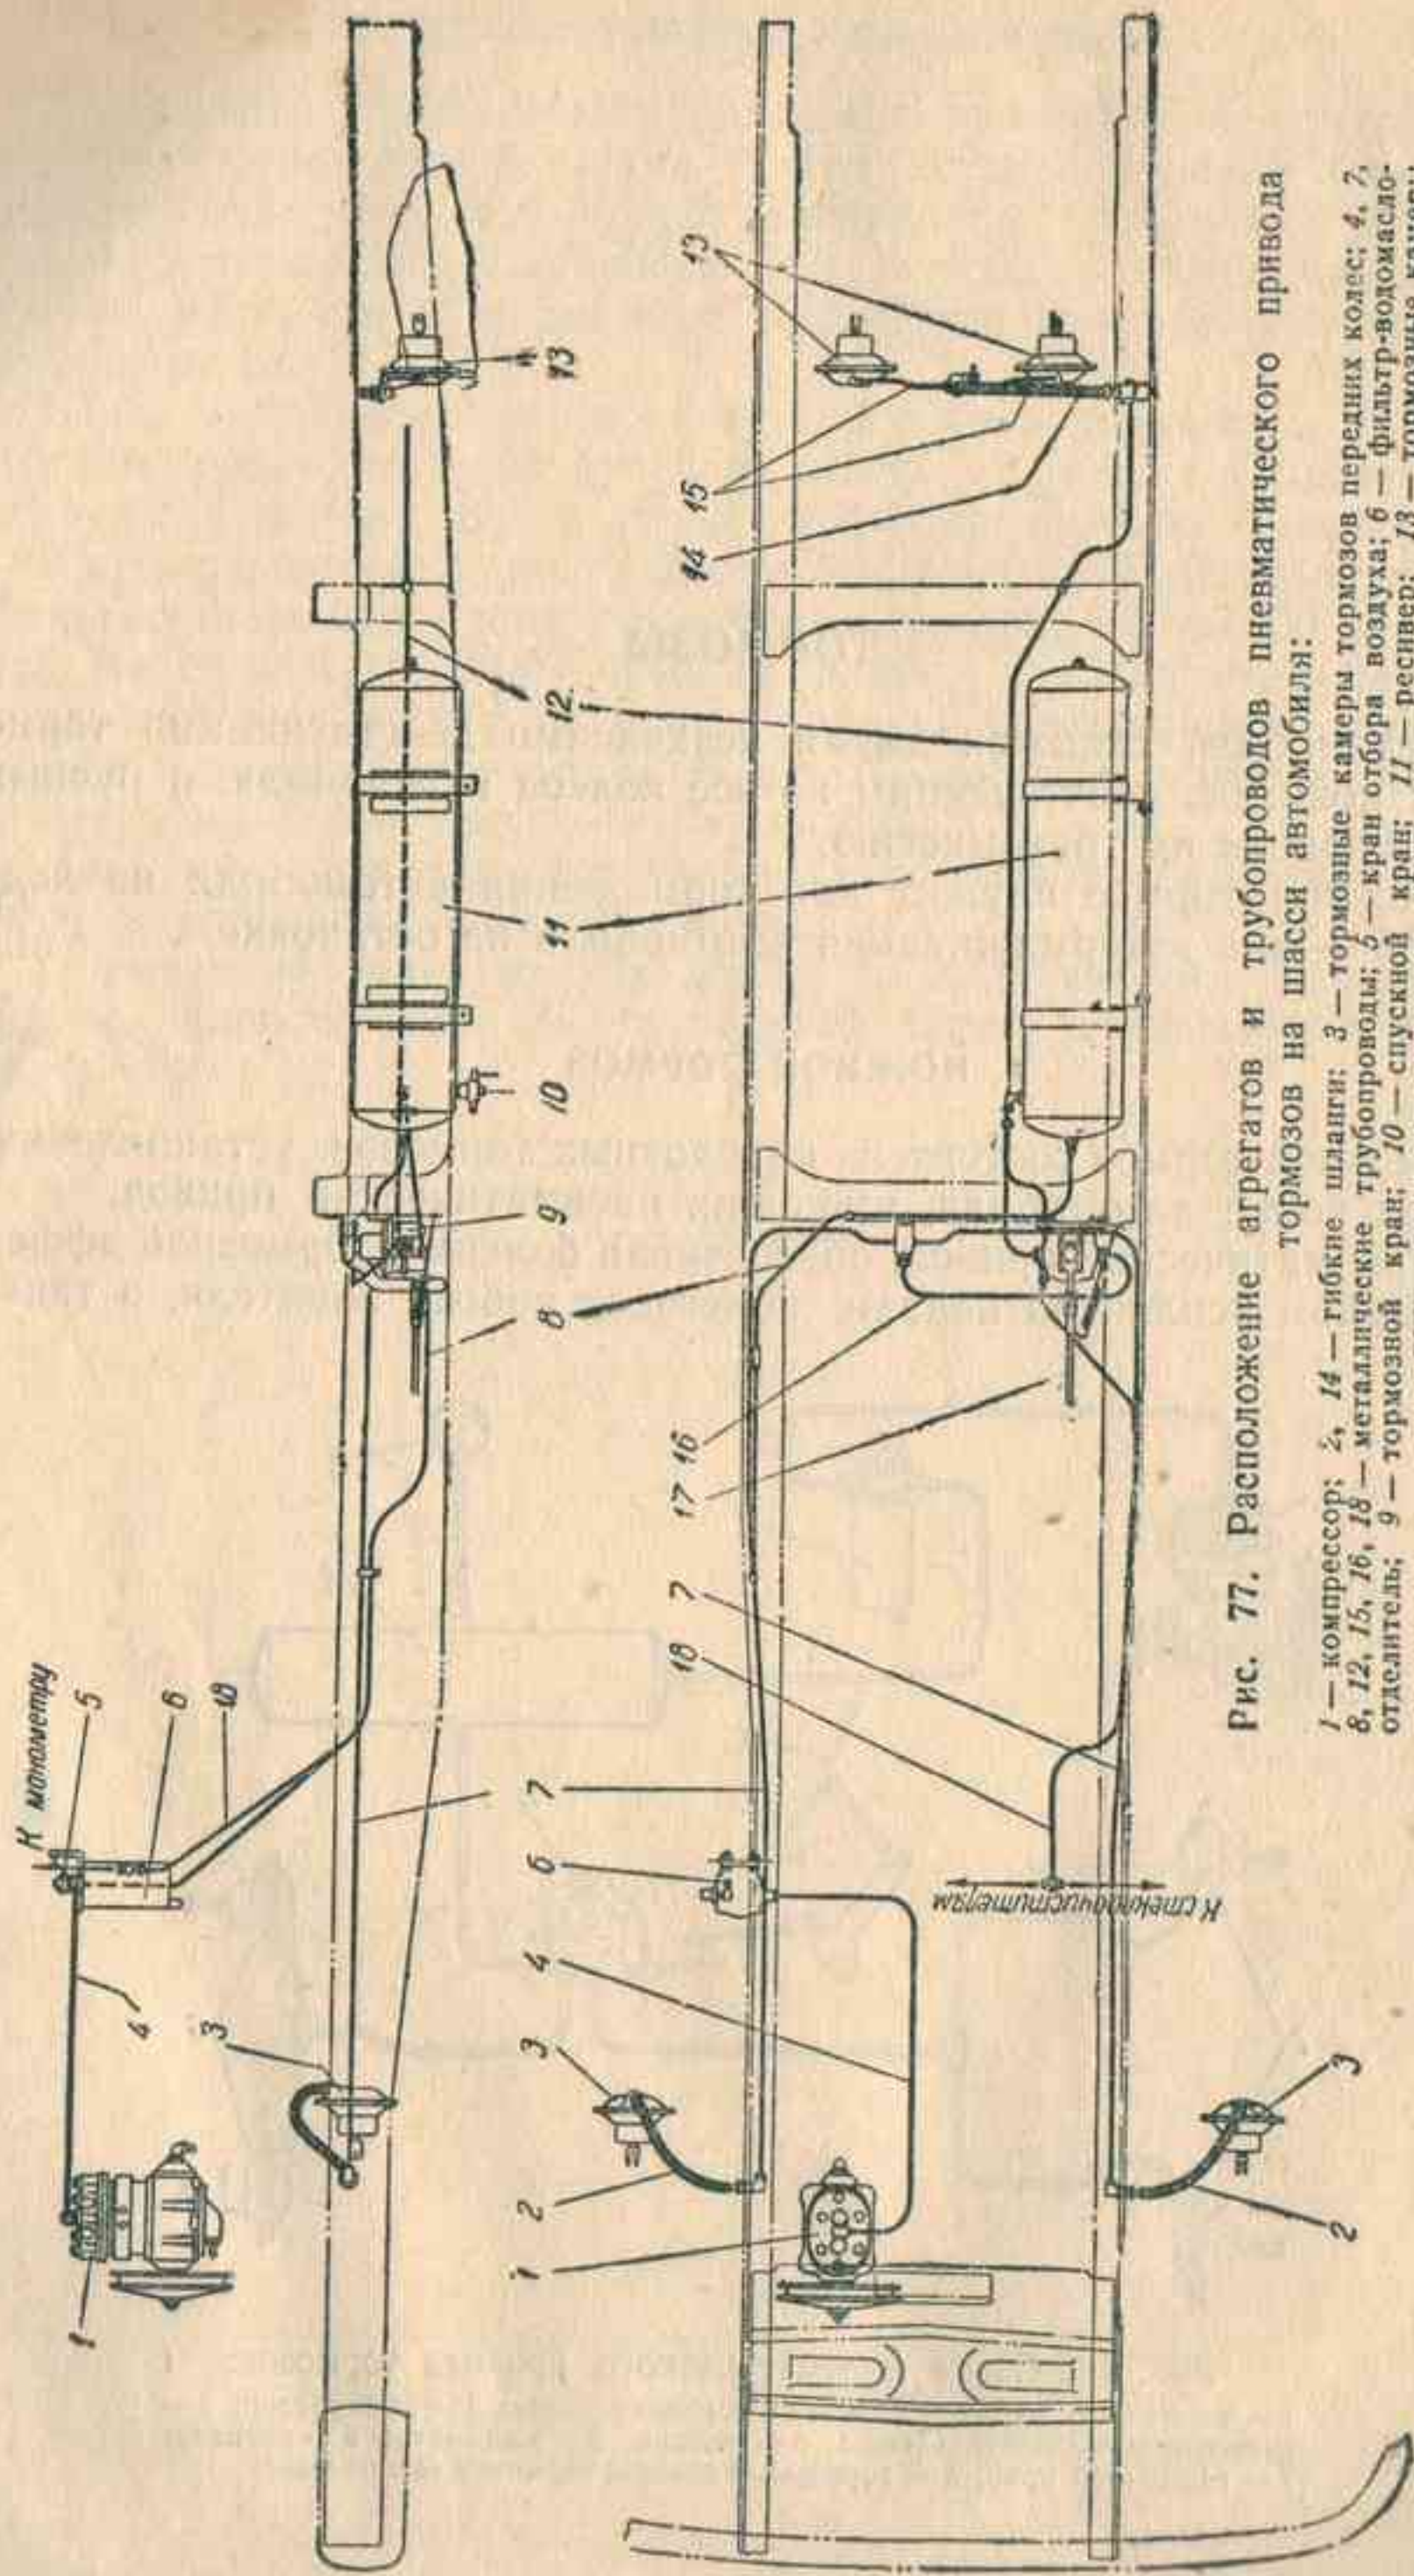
Расположение агрегатов и трубопроводов пневматического привода тормозов на шасси автомобиля:
